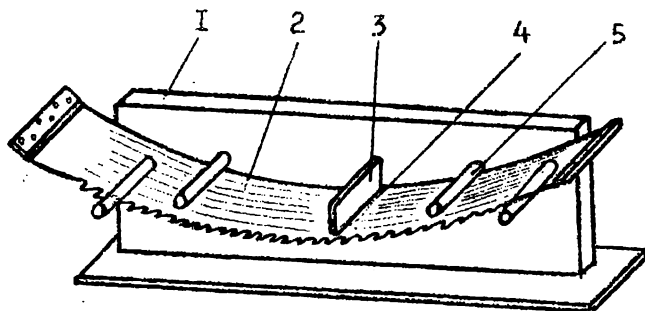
Приспособление для проверки степени вальцевания рамных пил:
